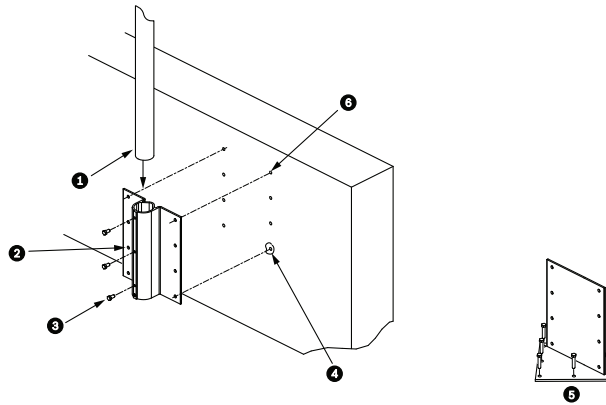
Подвесной кронштейн для монтажа на парапет и монтажная пластина для крыши
